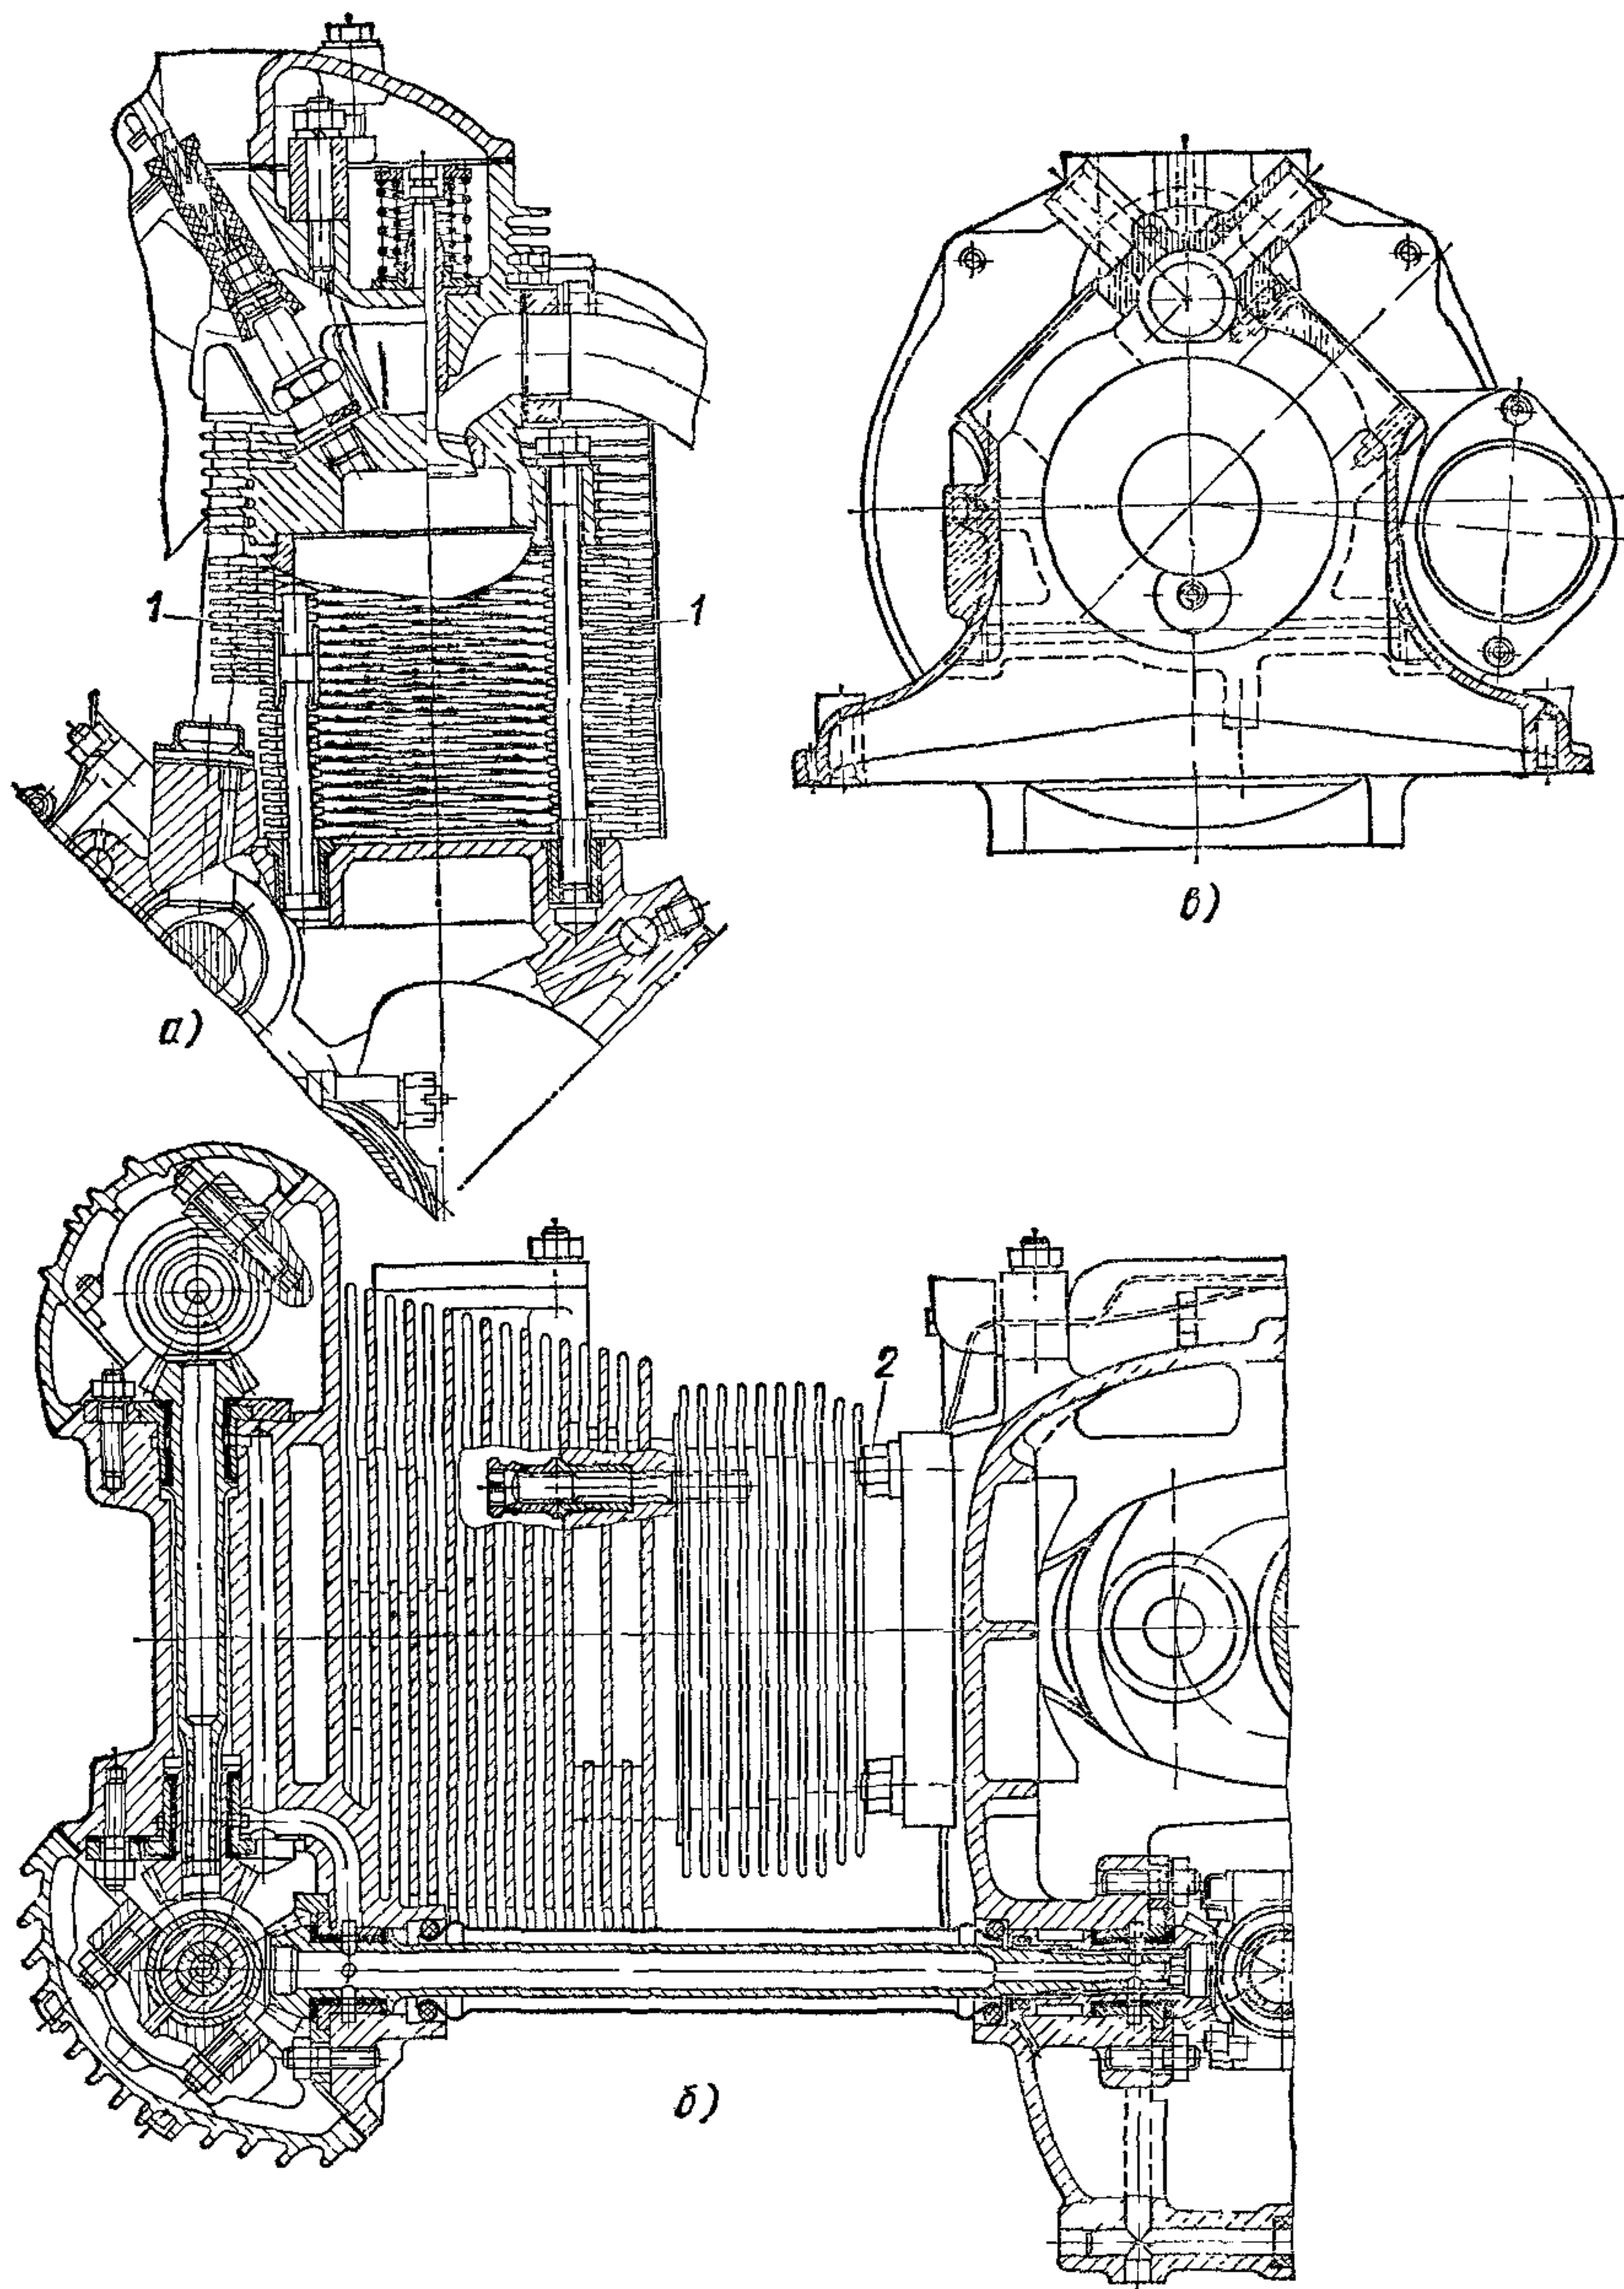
Цилиндры и картеры двигателей с воздушным охлаждением
